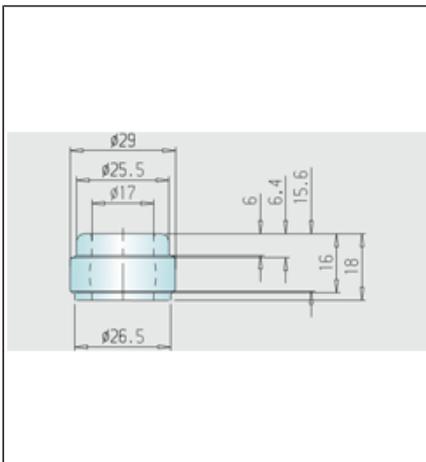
Boca da garrafa para tampadora de rolhas conforme DIN EN 12726
